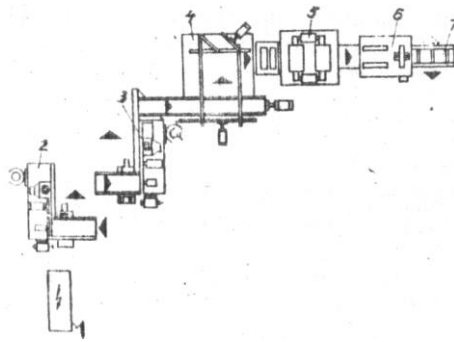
Схема лінії склеювання заготовок по довжині на зубчастий шип: 1 - пульт; 2, 3 - формування зубчастих шипів; 4 - з'єднання шипів; 5 - запресування; 6 - торцювання по довжині; 7 - приймальний роликостіл.
